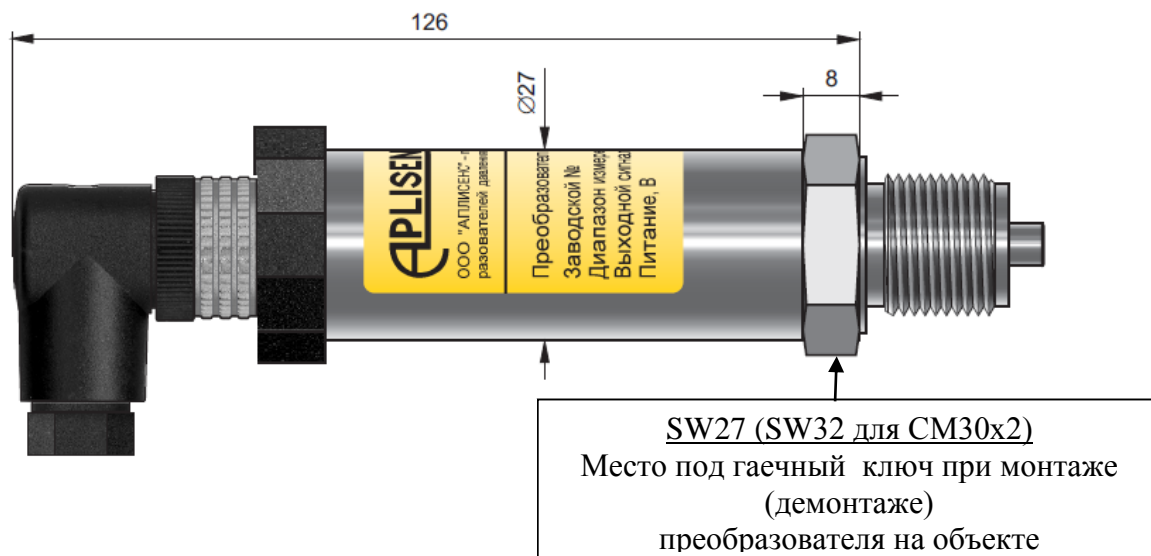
Внешний вид, установочные и присоединительные размеры преобразователя с присоединением РМ12
